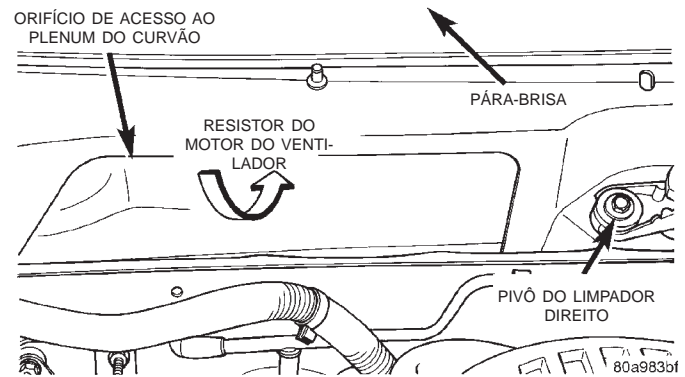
Remoção/Instalação do Resistor do Motor do Ventilador
